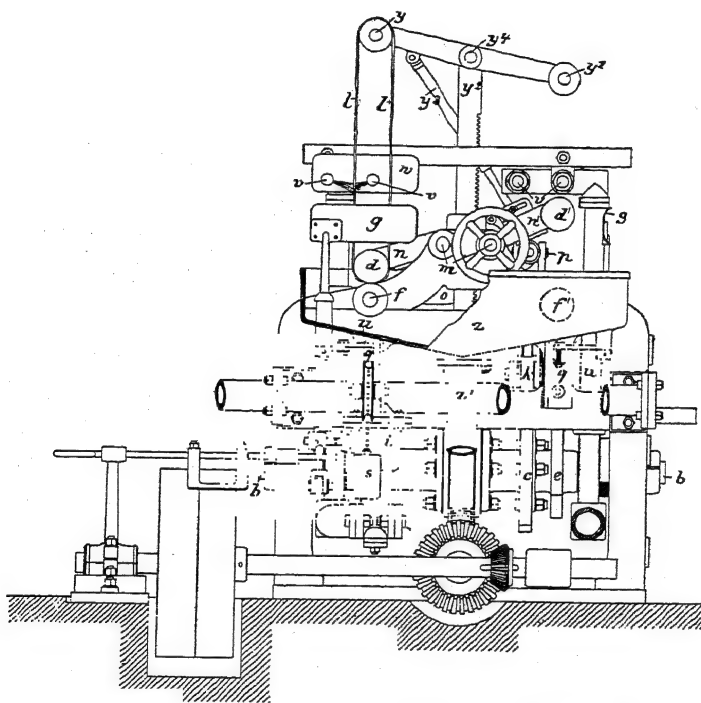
Garnwaschmaschine; Schnitt. (Sulzer.)
